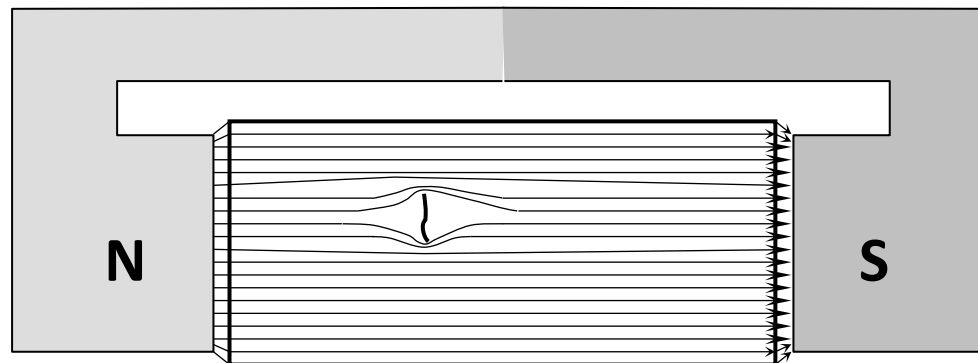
Pieza con una grieta en dirección perpendicular al campo magnético.
